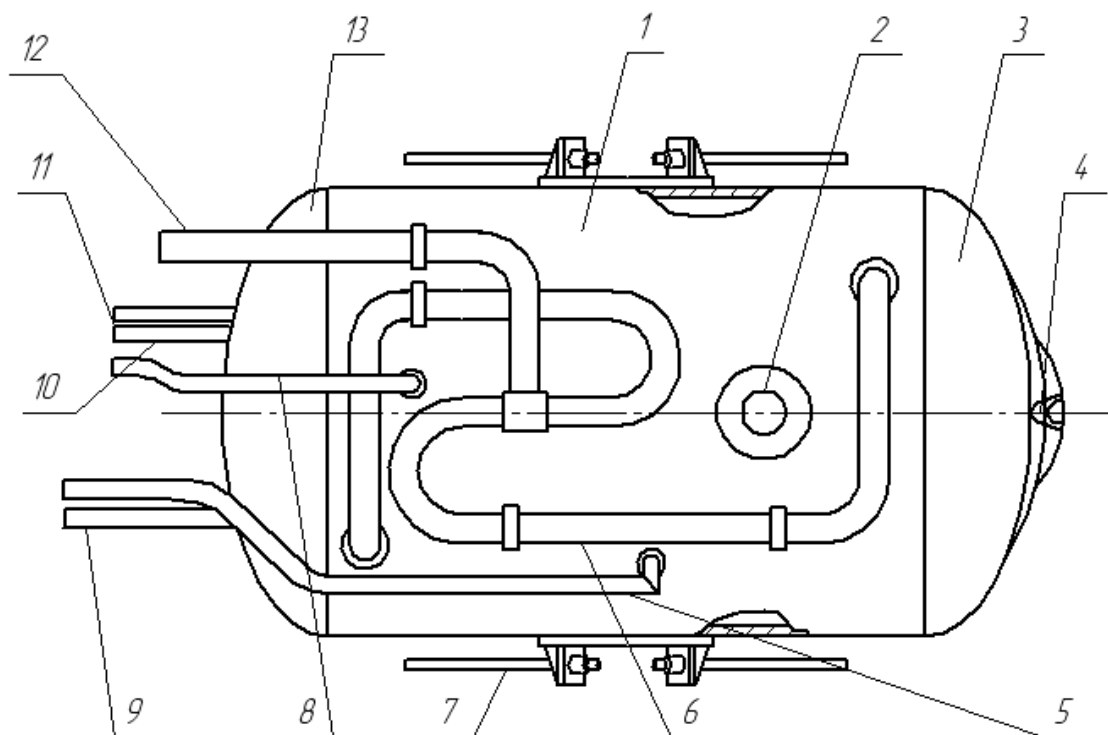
Схема резервуара ТРЖК-7М (вид сбоку):
